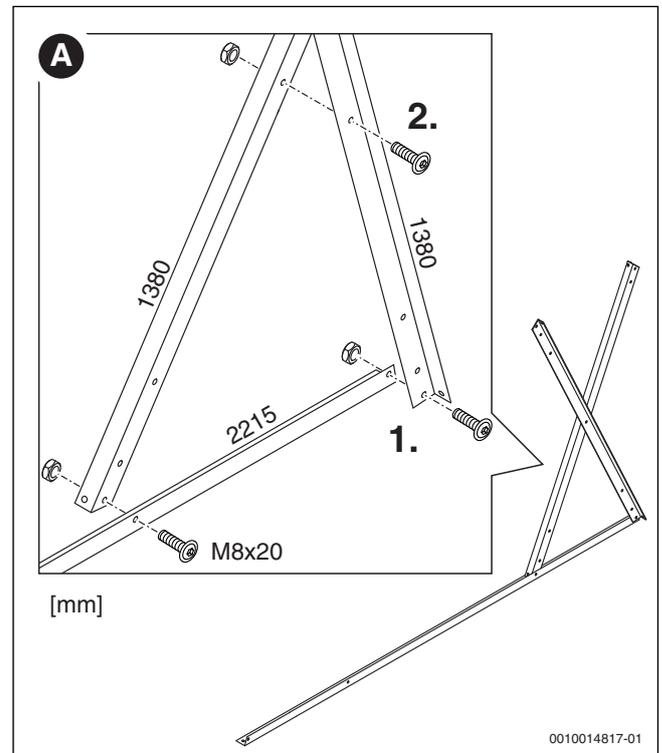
Serrer en croix sur le profilé de 2 215 mm (équerre A)
